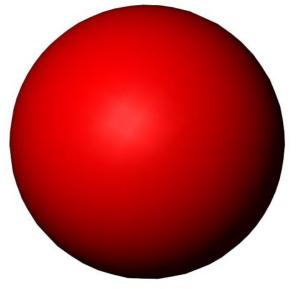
Модель детали 1, части 2: шарик подшипника
